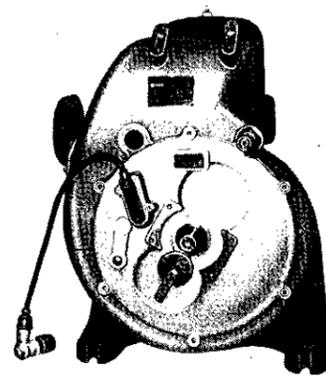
Gehäusedeckel mittels zweier Schraubenzieher abdrücken
